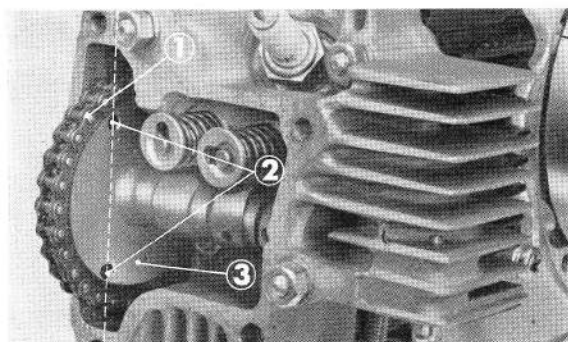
① chaîne de distribution ② ligne joignant les trous parallèle au plan du joint de culasse
